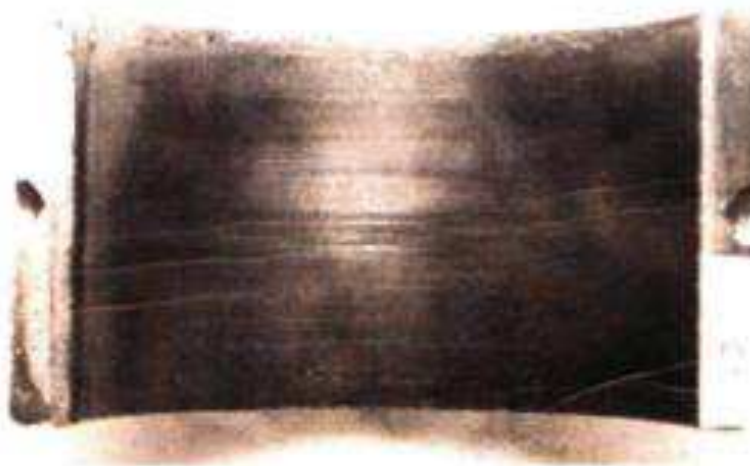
Поверхность втулки из металлофторопласта после испытаний со смазкой водой
